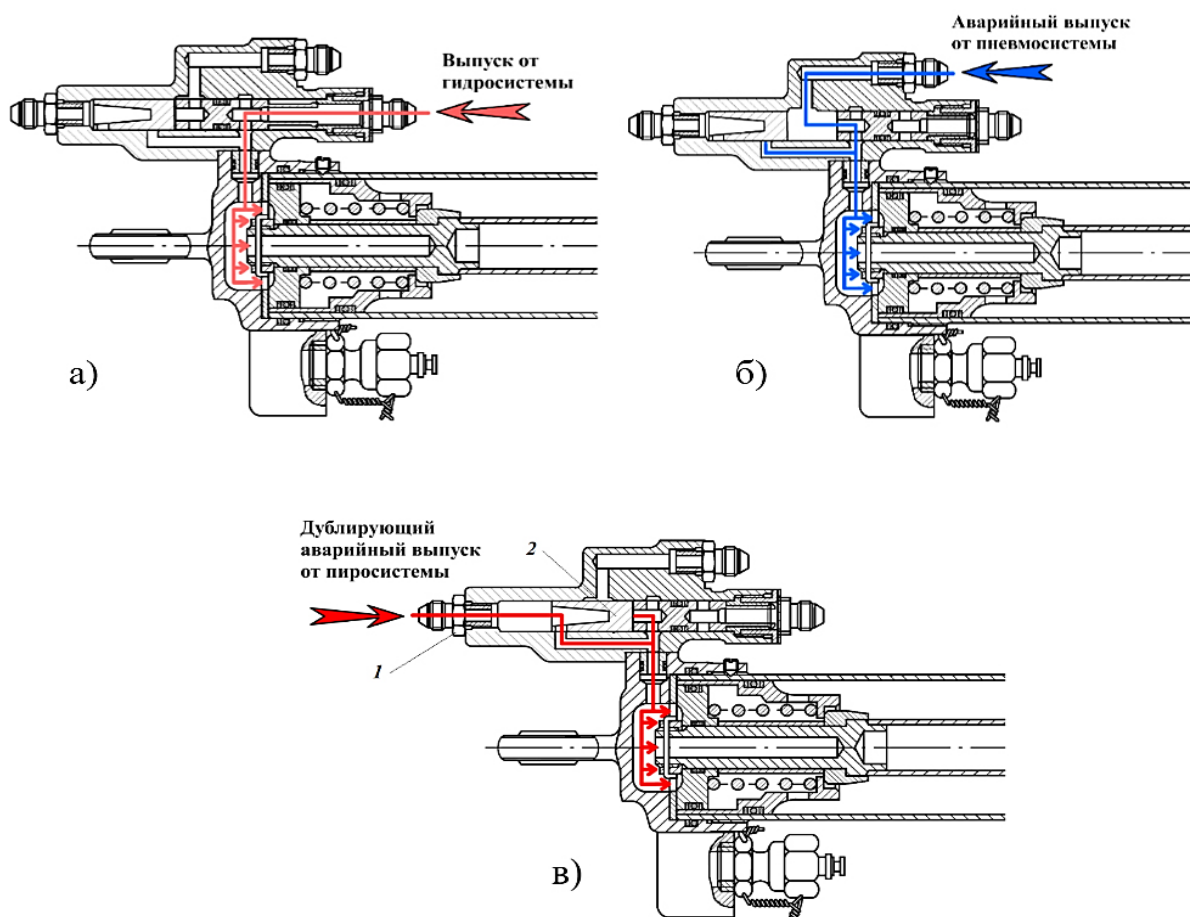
Цилиндр уборки-выпуска основных опор шасси с пиропереключателем:
